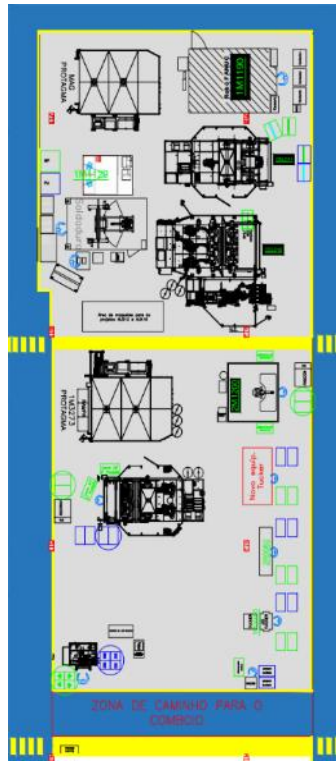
Proposta de *layout* para a soldadura MAG.
